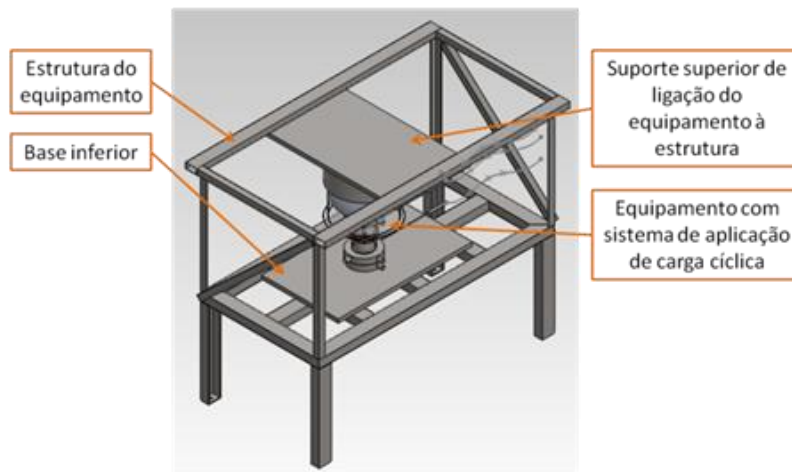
Desenho conceptual 3D de conjunto do equipamento concebido para a aplicação de carga cíclica para promover a soldadura por PDW.
